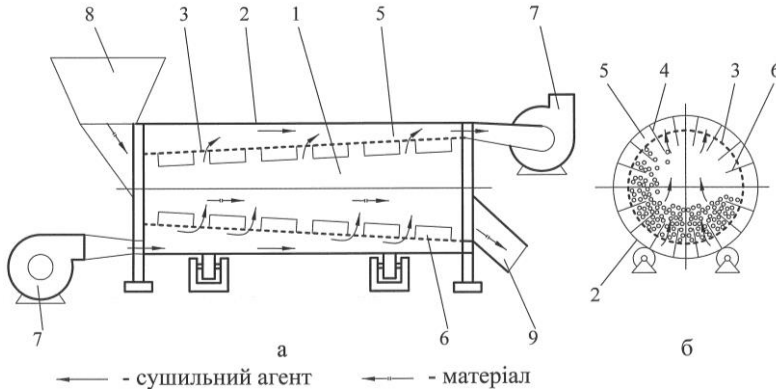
Барабанна сушарка: 1 – сушильний барабан; 2 – циліндричний кожух; 3 – перфорований конус; 4 – перегородка; 5 – секція; 6 – полицка; 7 – вентилятор; 8 – завантажувальний бункер; 9 – вивантажувальний патрубок
